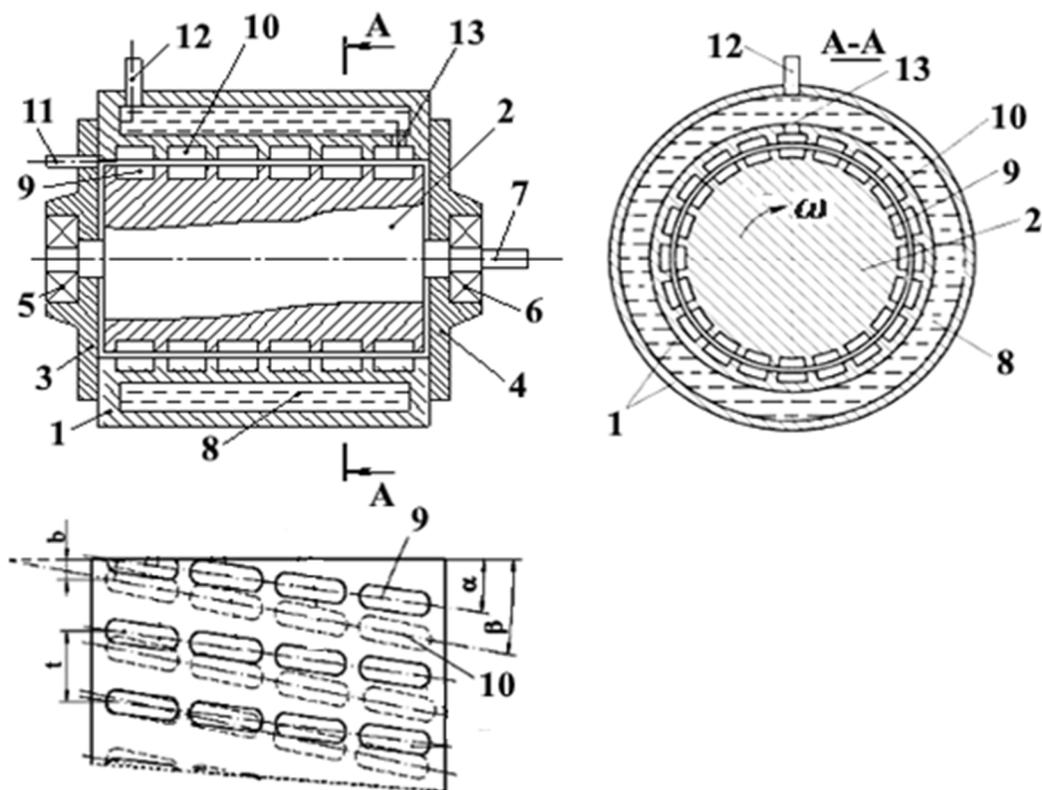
Общий вид гидродинамического нагревателя молока: 1 – статор нагревателя; 2 – ротор; 3 и 4 – передняя и задняя крышки; 5 и 6 – передний и задний подшипники; 7 – вал; 8 – полость в статоре; 9 и 10 – ячейки ротора и статора; 11 и 12 – патрубки подачи и отвода молока; 13 – отверстие
